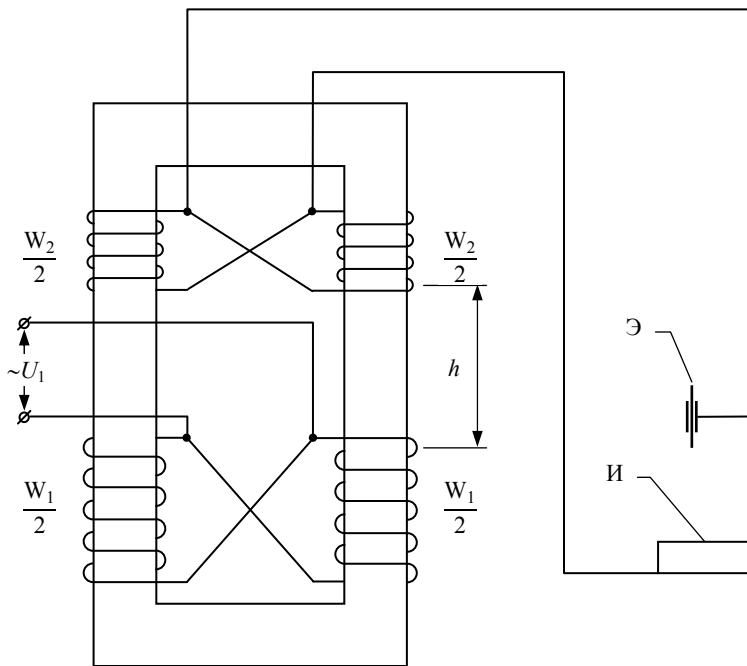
Сварочный трансформатор с подвижными катушками обмоток
